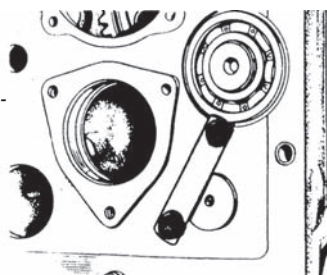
Выпрессовка подшипника № 60210, замена гнезда подшипника промежуточного вала.
